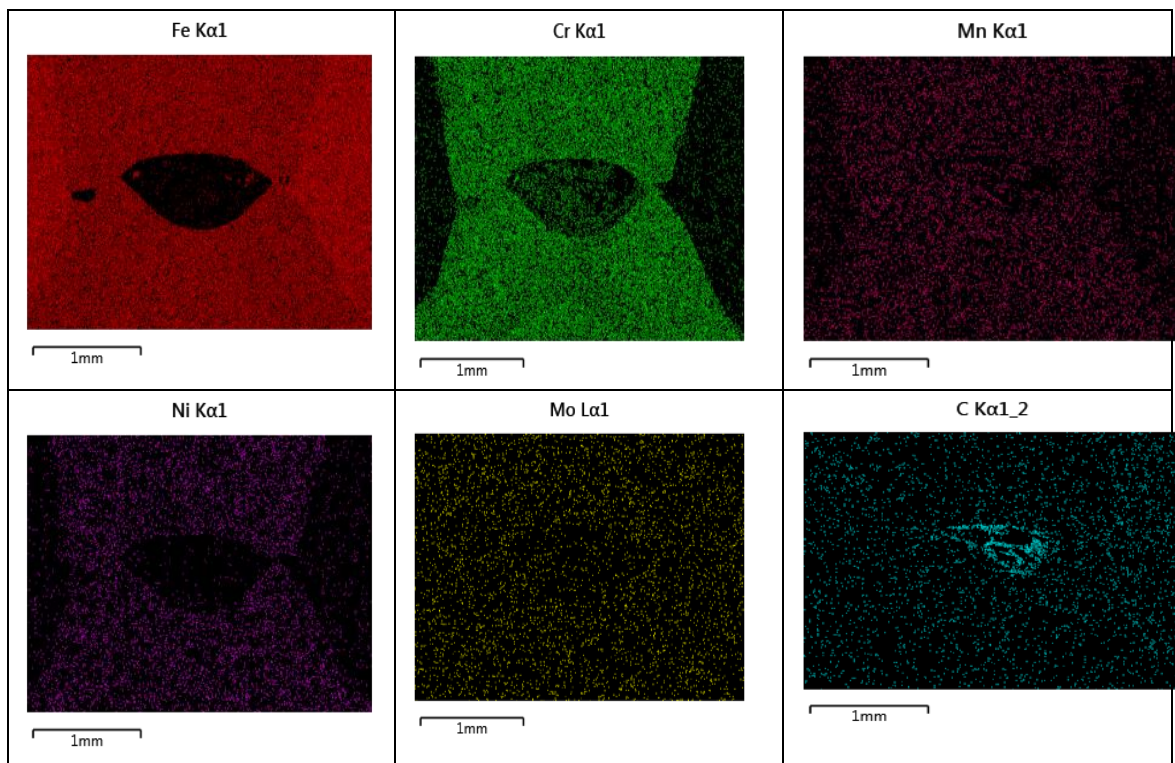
EDS por elementos en la junta de la unión soldada con un electrodo E312-16
